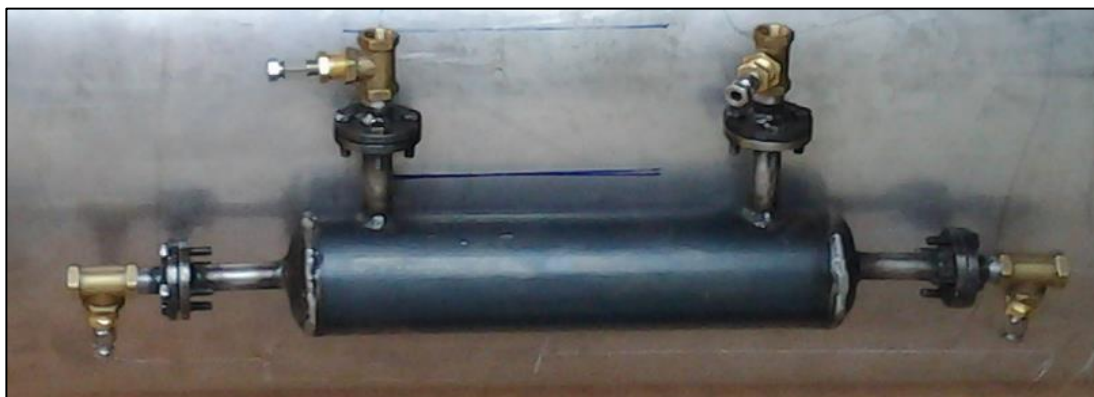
Instalación de uniones tipo T, bushings y acoples de compresión
